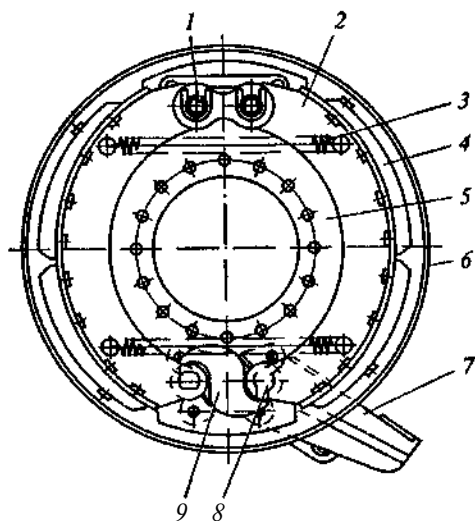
Колесный тормозной механизм грузового автомобиля КамАЗ:
